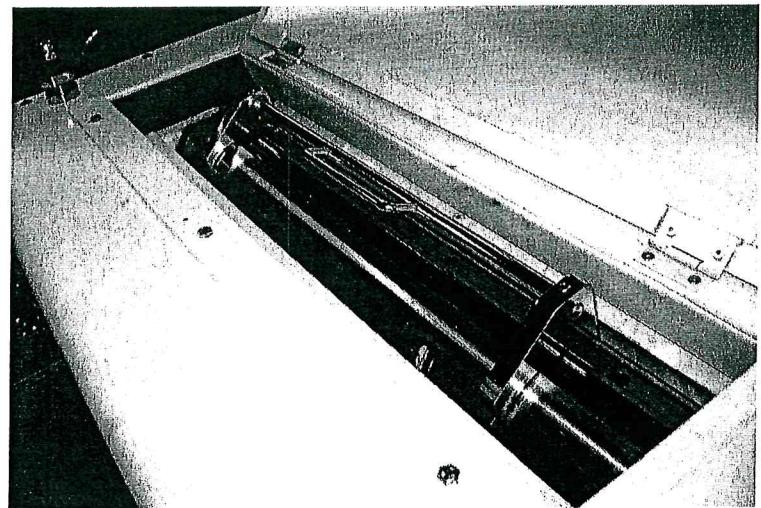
Установка и выверка ножей в корпусе ножевого вала
